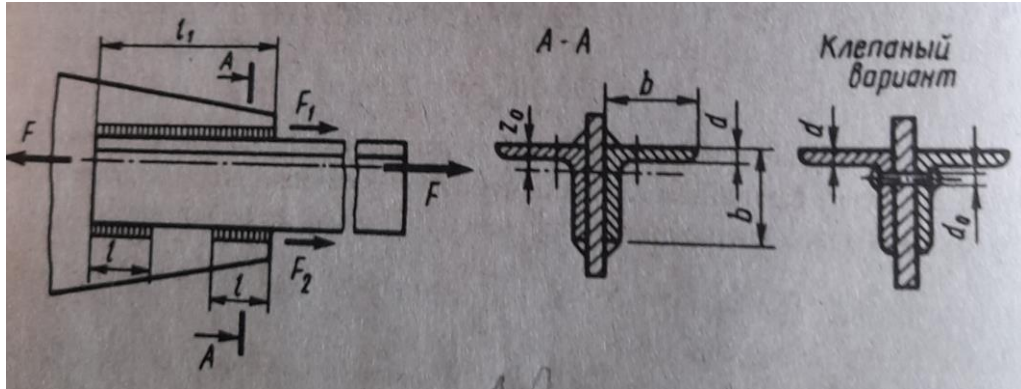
Рассматриваемый сварной шов
